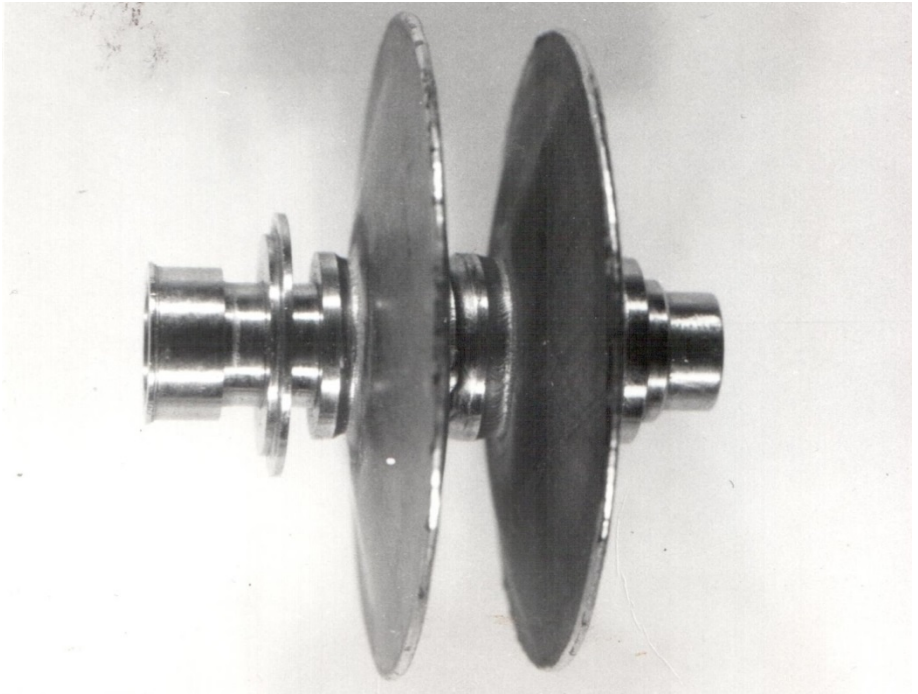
Общий вид штамповарного фильтра из стали 12X18H10T, обеспечивающего тонкость очистки 10...12 мкм
